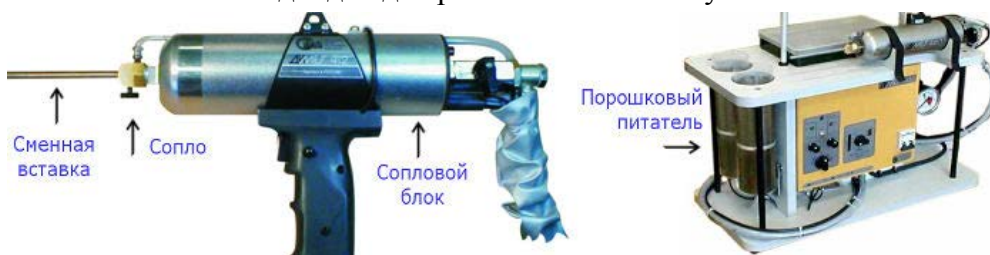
Установка для газодинамического напыления (общий вид)
